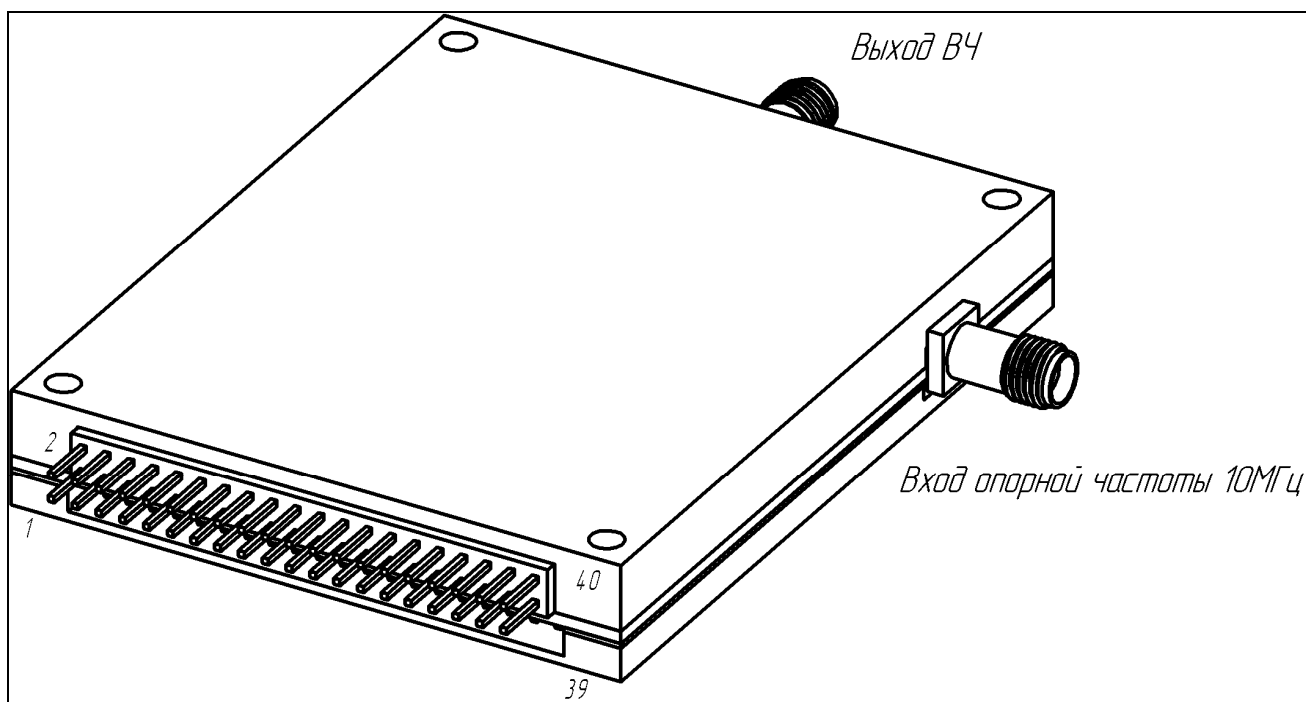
Эскиз внешнего вида синтезатора в корпусе.
